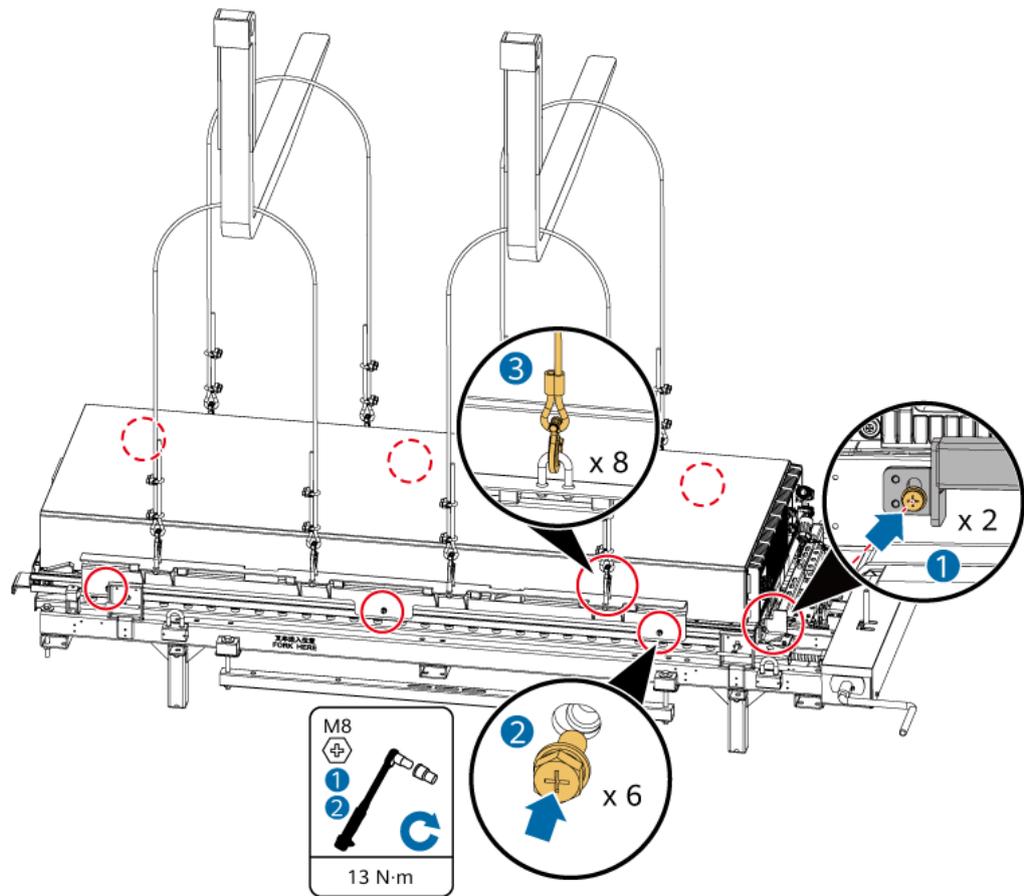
Instalación de la biela del grupo de baterías y la biela del contenedor
